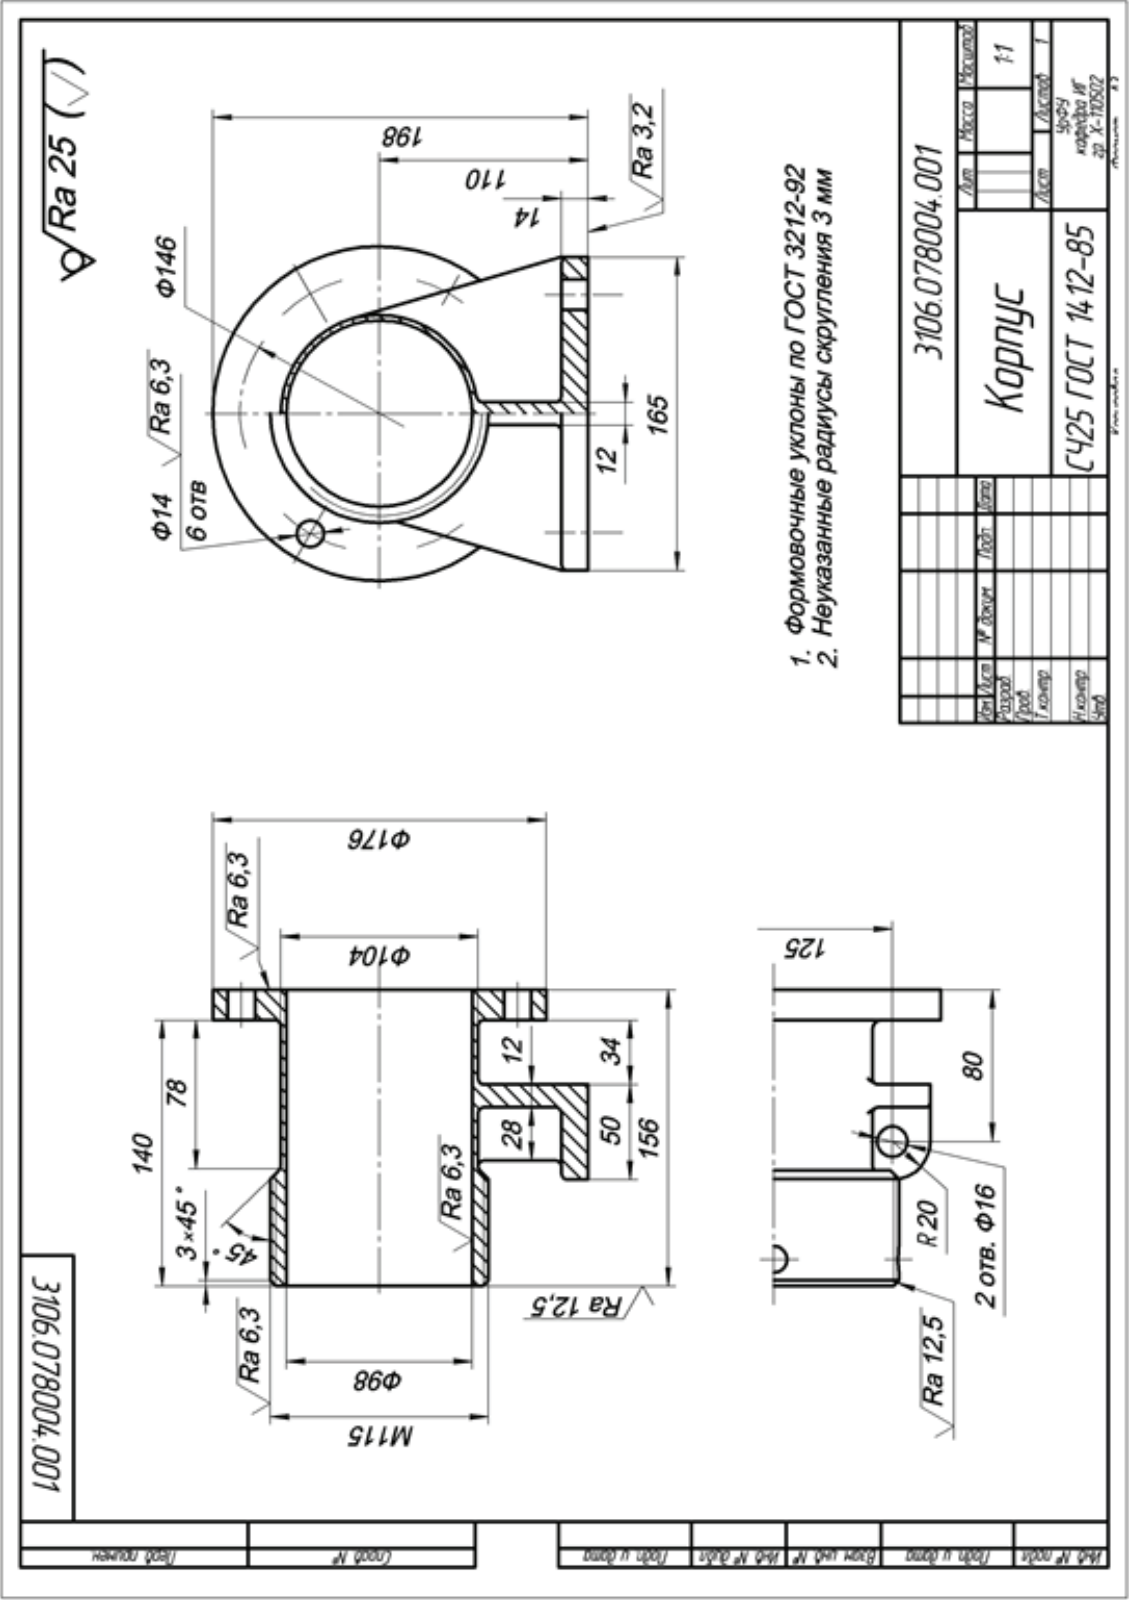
Пример учебного чертежа литой детали «Корпус»
